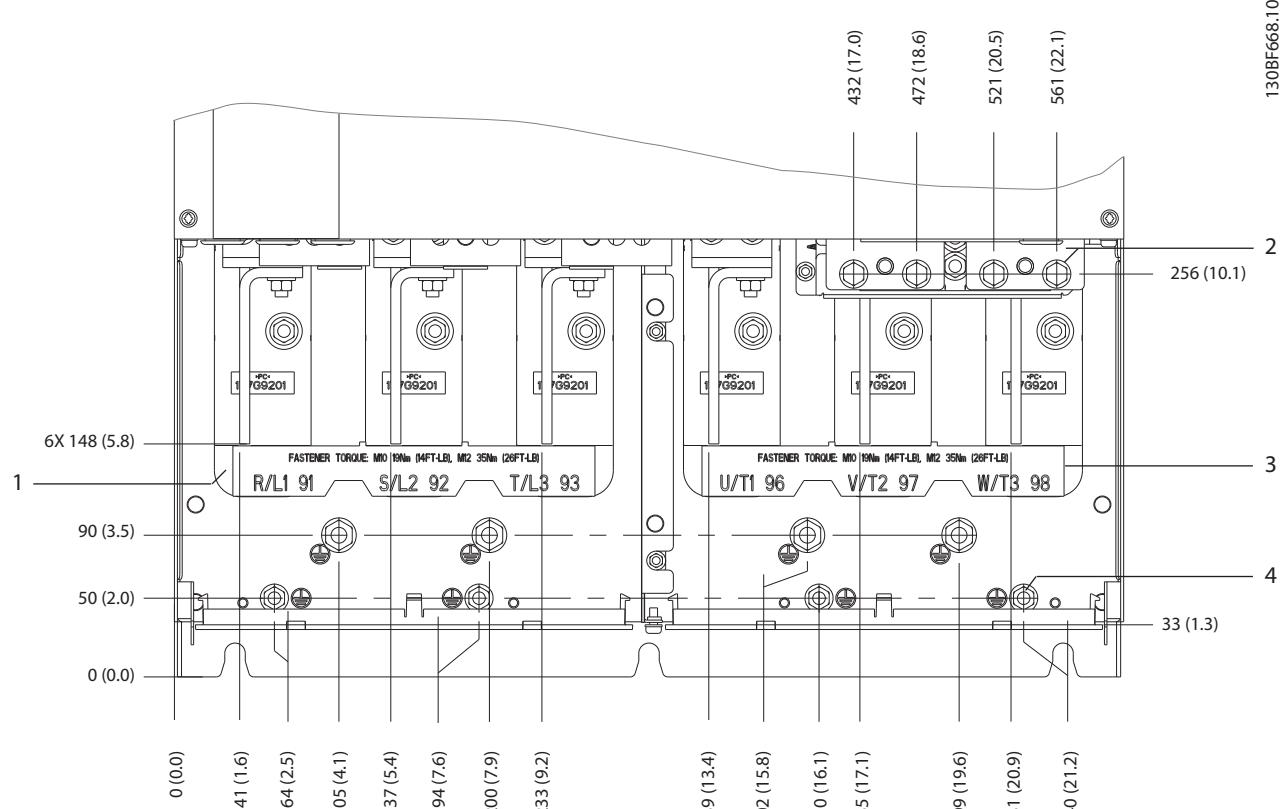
Dimensi Terminal Sumber Listrik, Motor, dan Pemburni E3h (Tampak Samping)
